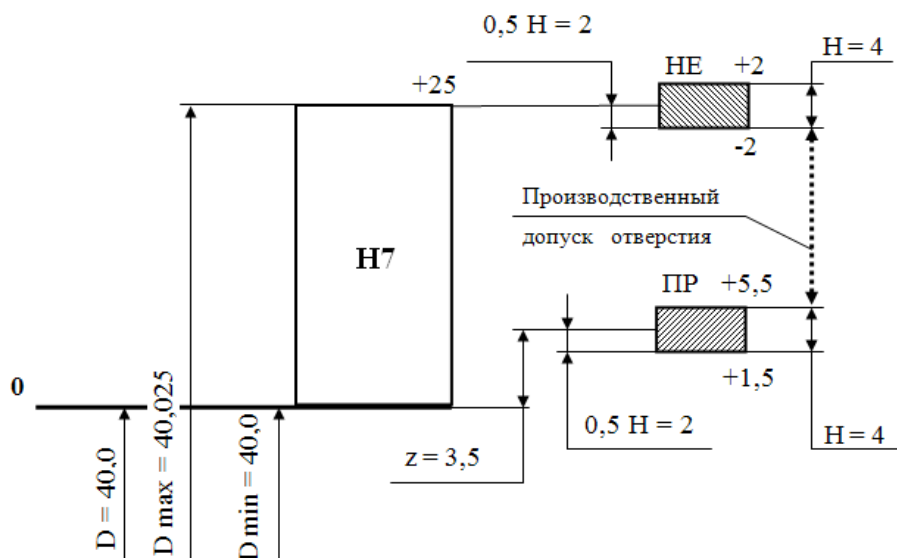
Схема расположения полей допусков на изготовление калибра - пробки для контроля отверстия $\varnothing 40 H7 (+0,025)$
